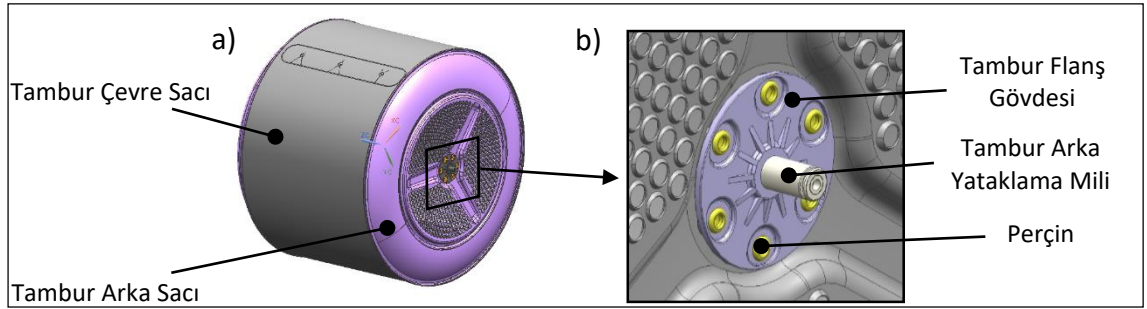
Tambur çevre sacı ile ilişkili tambur grubu parçaları
